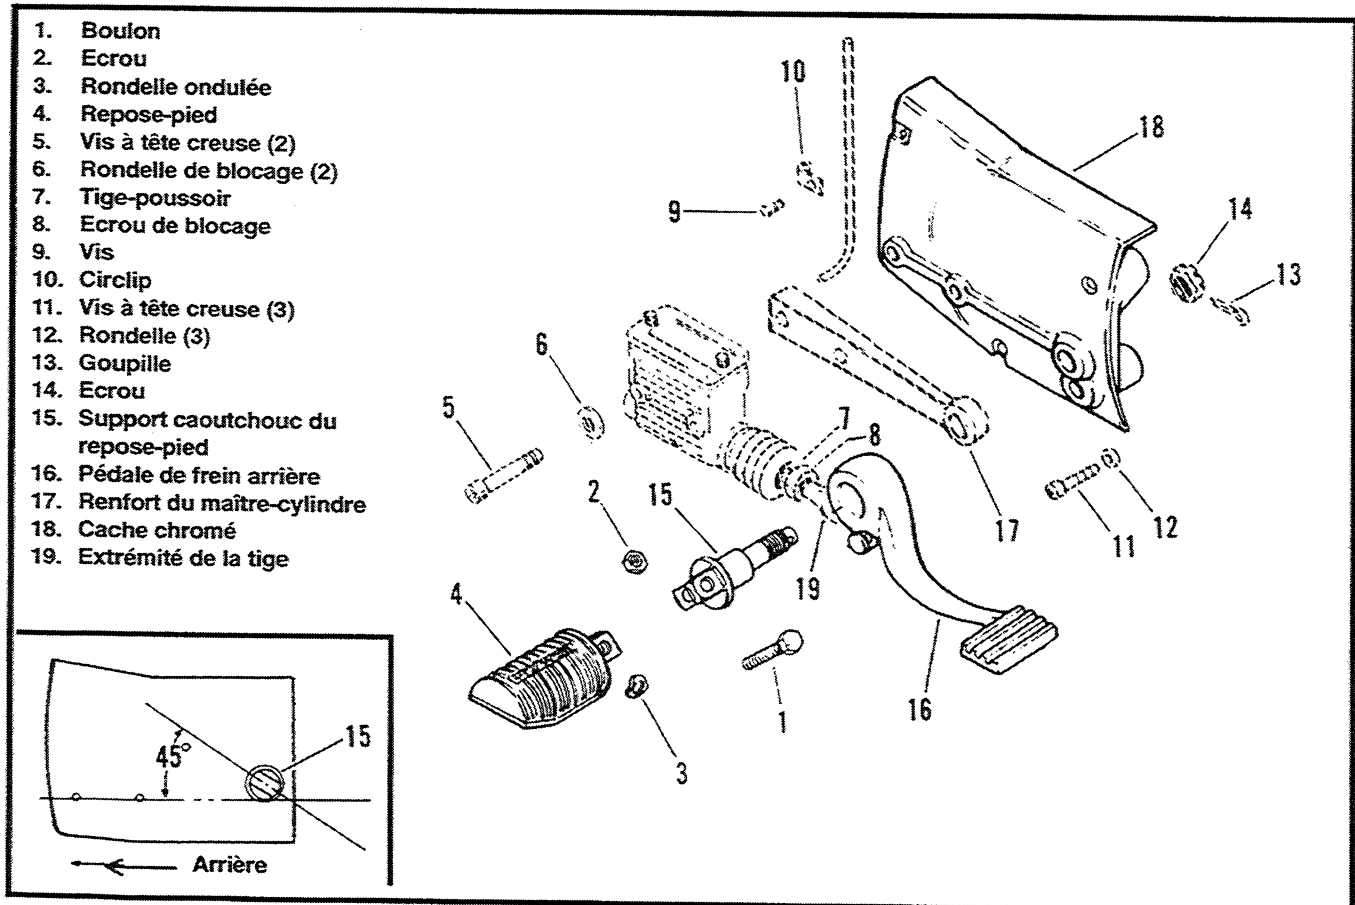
Montage du repose-pied, des tringles freins arrière, et du cache chromé
